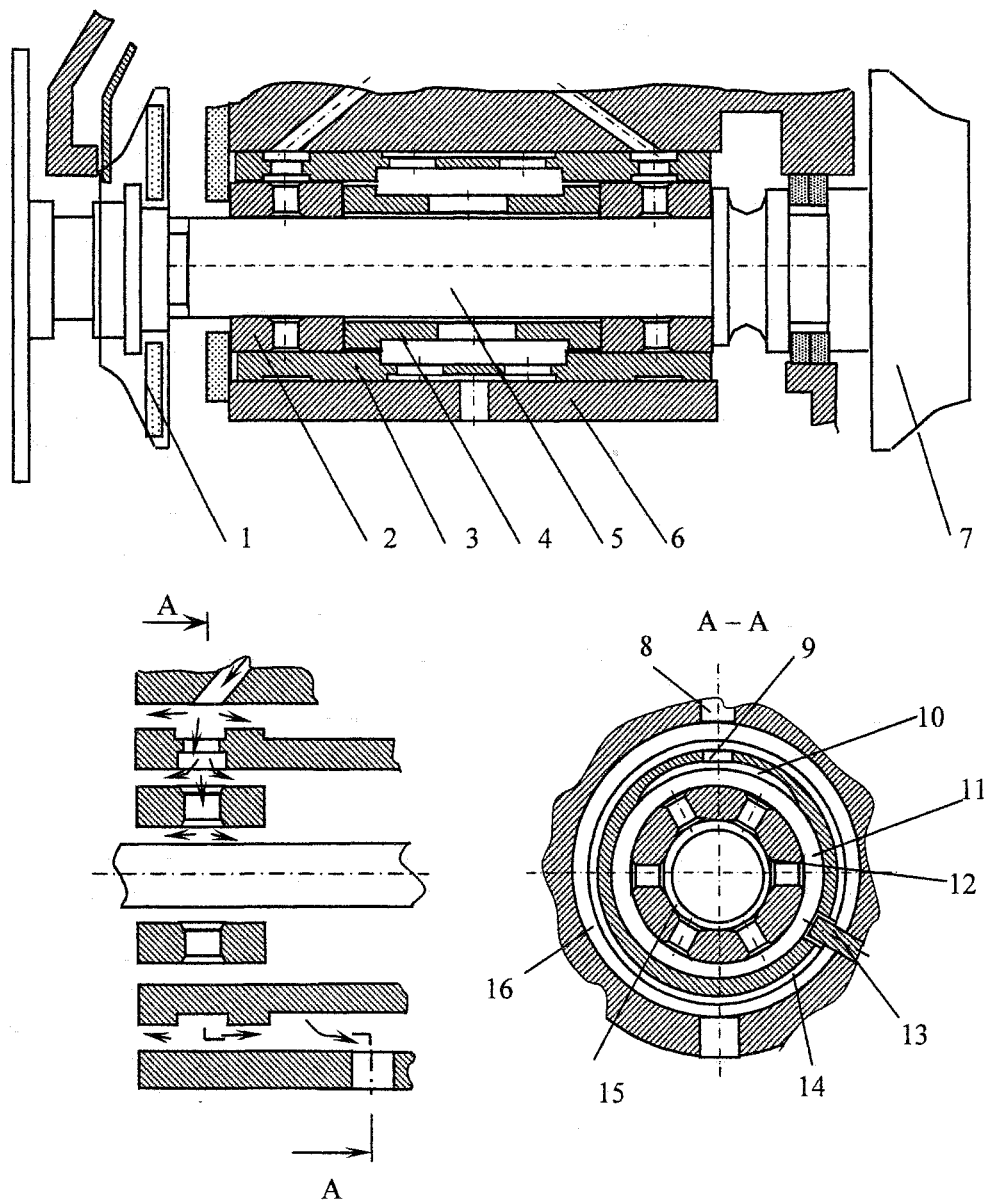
Конструкция ротора на подшипниках с пакетом плавающих втулок: 1 – компрессорное колесо; 2 – плавающая вращающаяся втулка; 3 – плавающая невращающаяся моновтулка; 4 – дистанционная втулка; 5 – ротор; 6 – средний корпус турбокомпрессора; 7 – турбинное колесо; 8, 9, 12 – отверстия для подачи смазки; 10, 14 – сегментная, кольцевая канавки; 11, 15, 16 – смазочные слои; 13 – штифт
